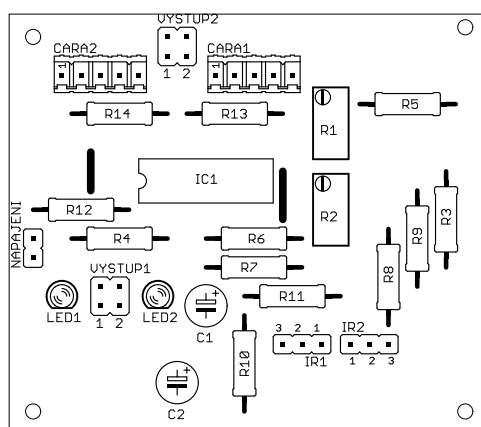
Deska plošného spoje hotového zařízení připojeného k počítači - vrstva BOTTOM
